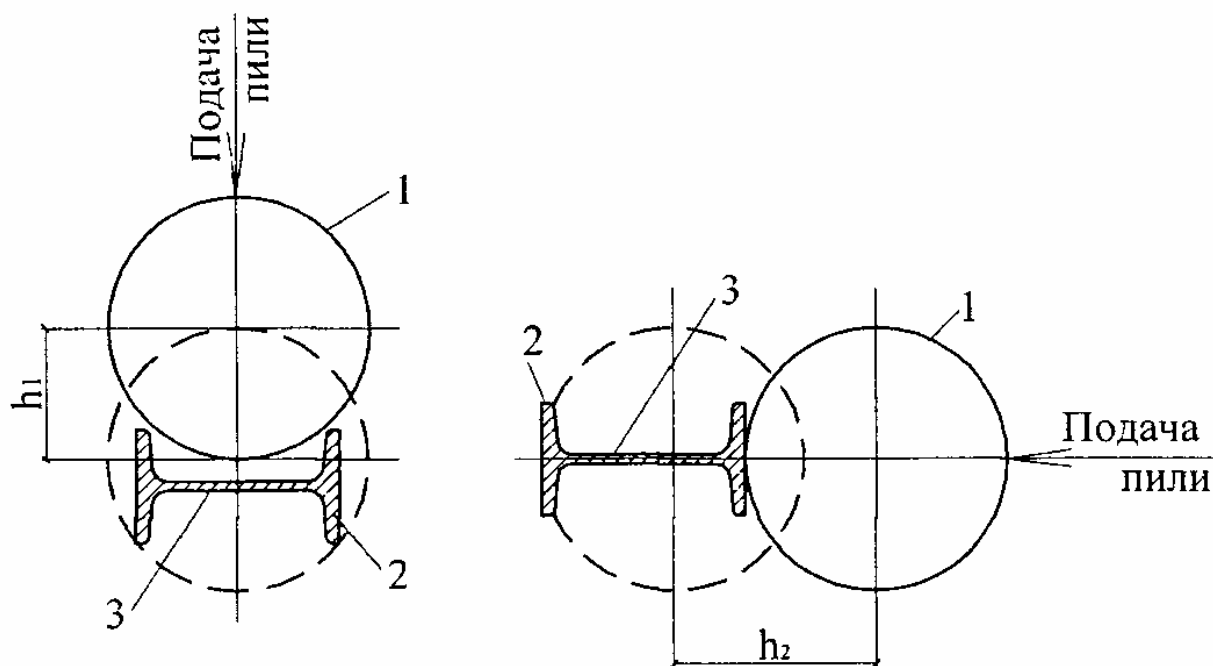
Схема високоточного різання дисковими пилами; 1 - диск; 2 - полиця; 3 - стінка профілю
